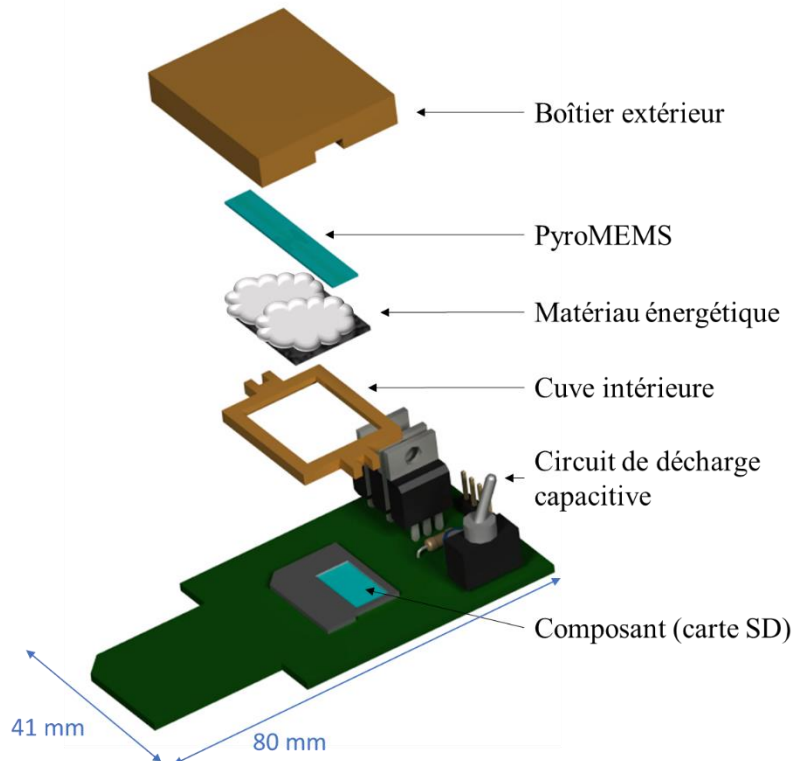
Schéma en vue explosé présentant l'assemblage et l'intégration du prototype de test de l'USD
